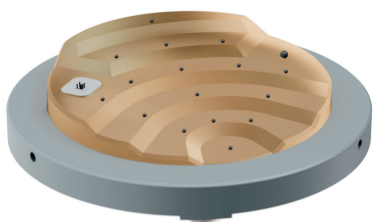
Prüfkörper „Arena“: stufenförmiger Grundkörper mit dimensionellen Anordnung von Kugeln © Saphirwerk
